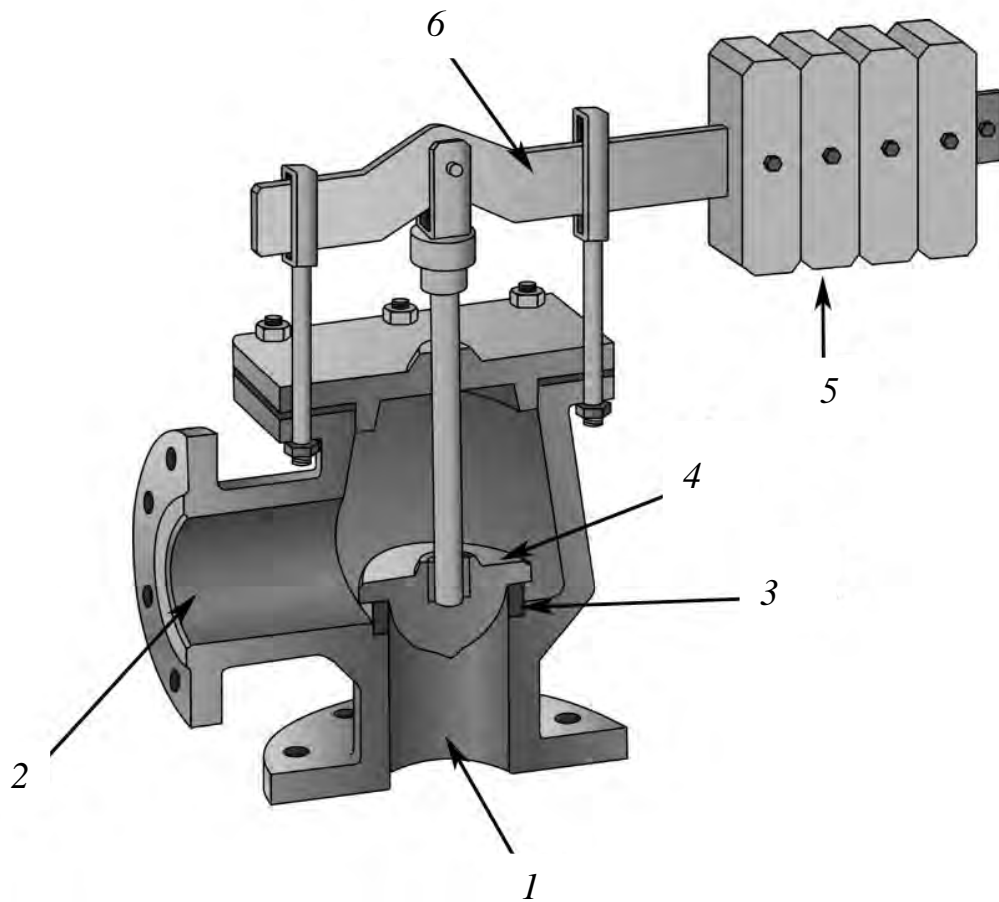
Предохранительный клапан: 1 – впускное отверстие; 2 – выпускное отверстие; 3 – седло клапана; 4 – тарелка клапана; 5 – груз; 6 – рычаг
